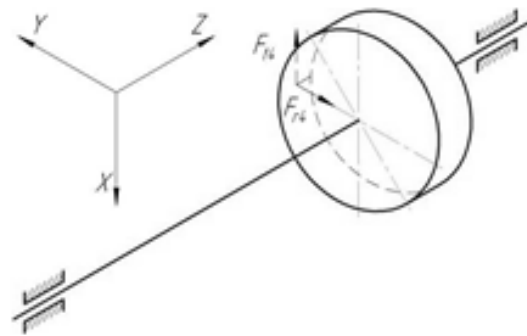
Силова схема тихохідного вала циліндричної передачі
